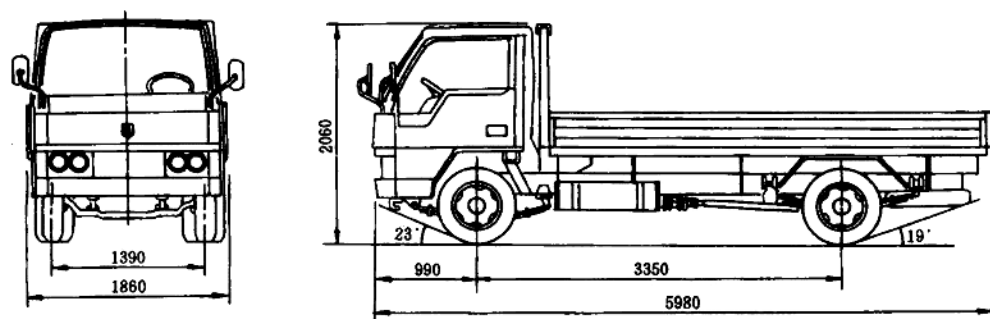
5 解放 CA1043L₂ 型载货汽车外形尺寸
